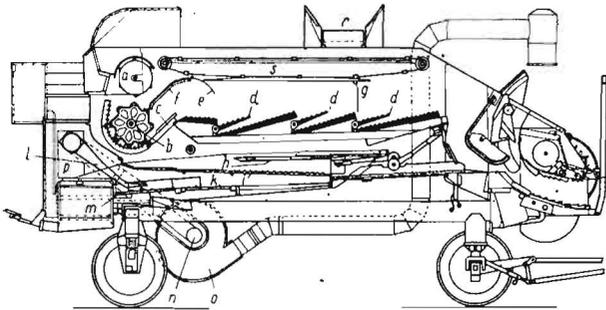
Schnittzeichnung der Dreschmaschine K 117
